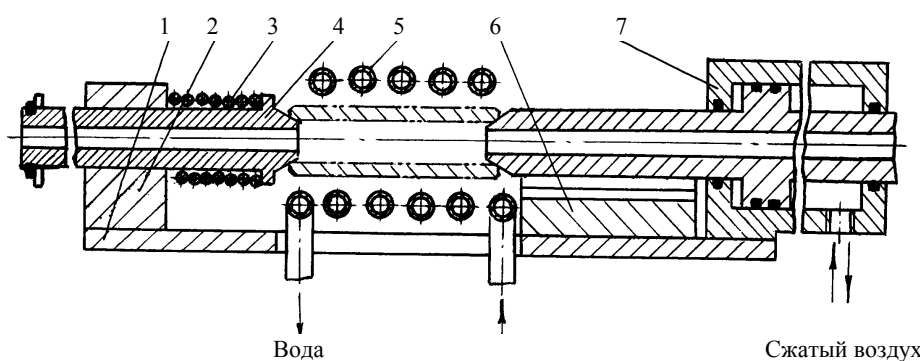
Схема станда для термопластической раздачи поршневых пальцев: 1 – плита; 2 – кронштейн; 3 – пружина; 4 – полый шток; 5 – индуктор; 6 – направляющая призма; 7 – пневмоцилиндр
